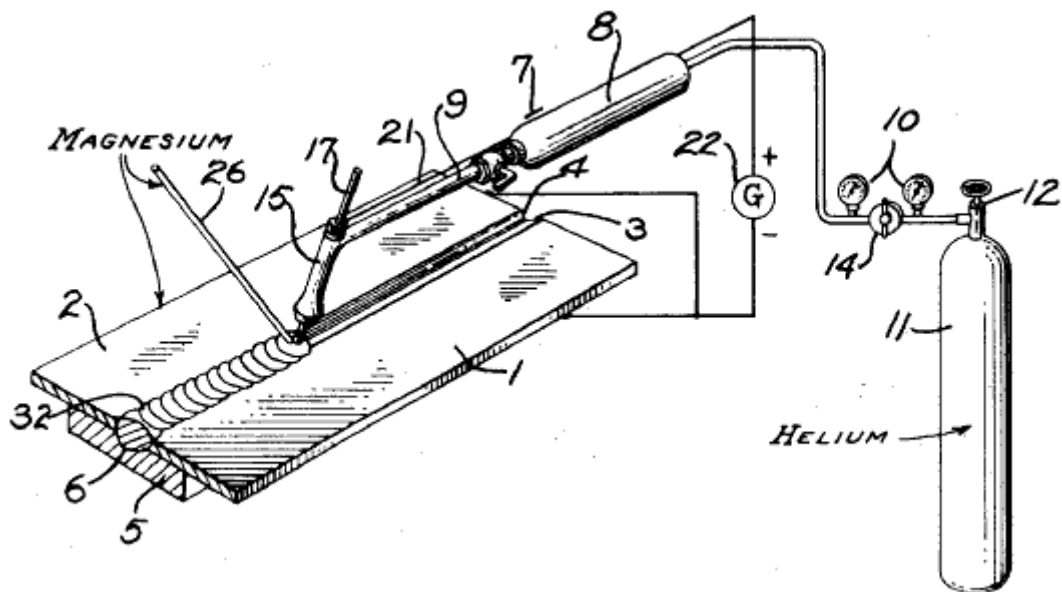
Perspetiva esquemática da soldadura TIG [5]
